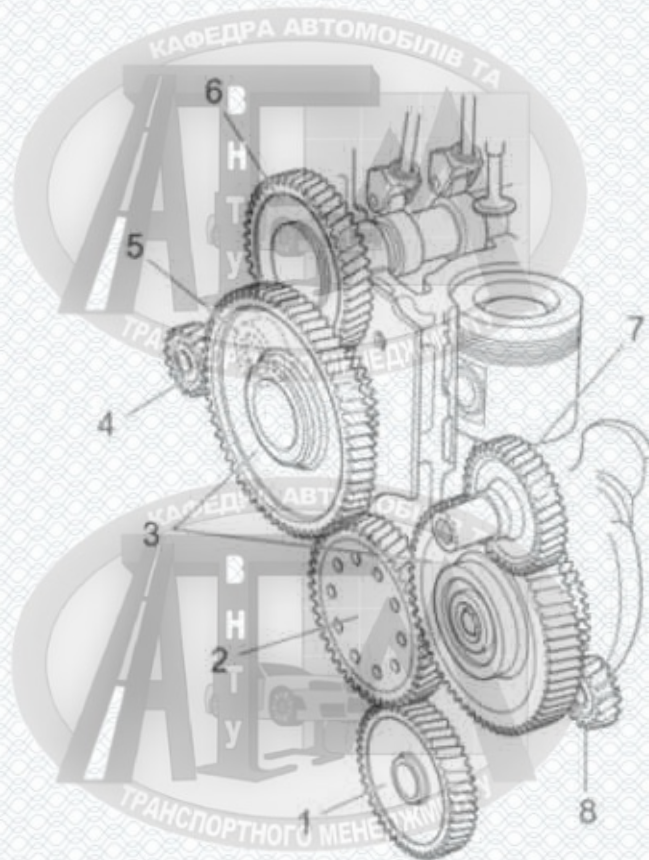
Особливості конструкції газарозподільного механізму, що використовується на рядних двигунах SCANIA: 1 - шестерня приводу масляного насоса; 2 - шестерня колінчастого вала; 3 - проміжна шестерня; 4 - шестерня приводу гідравлічного насоса; 5 - шестерня приводу компресора; 6 - шестерня приводу розподільного вала; 7 - коробка відбору потужності; 8 - шестірна приводу компресора (блок циліндрів другого покоління).
